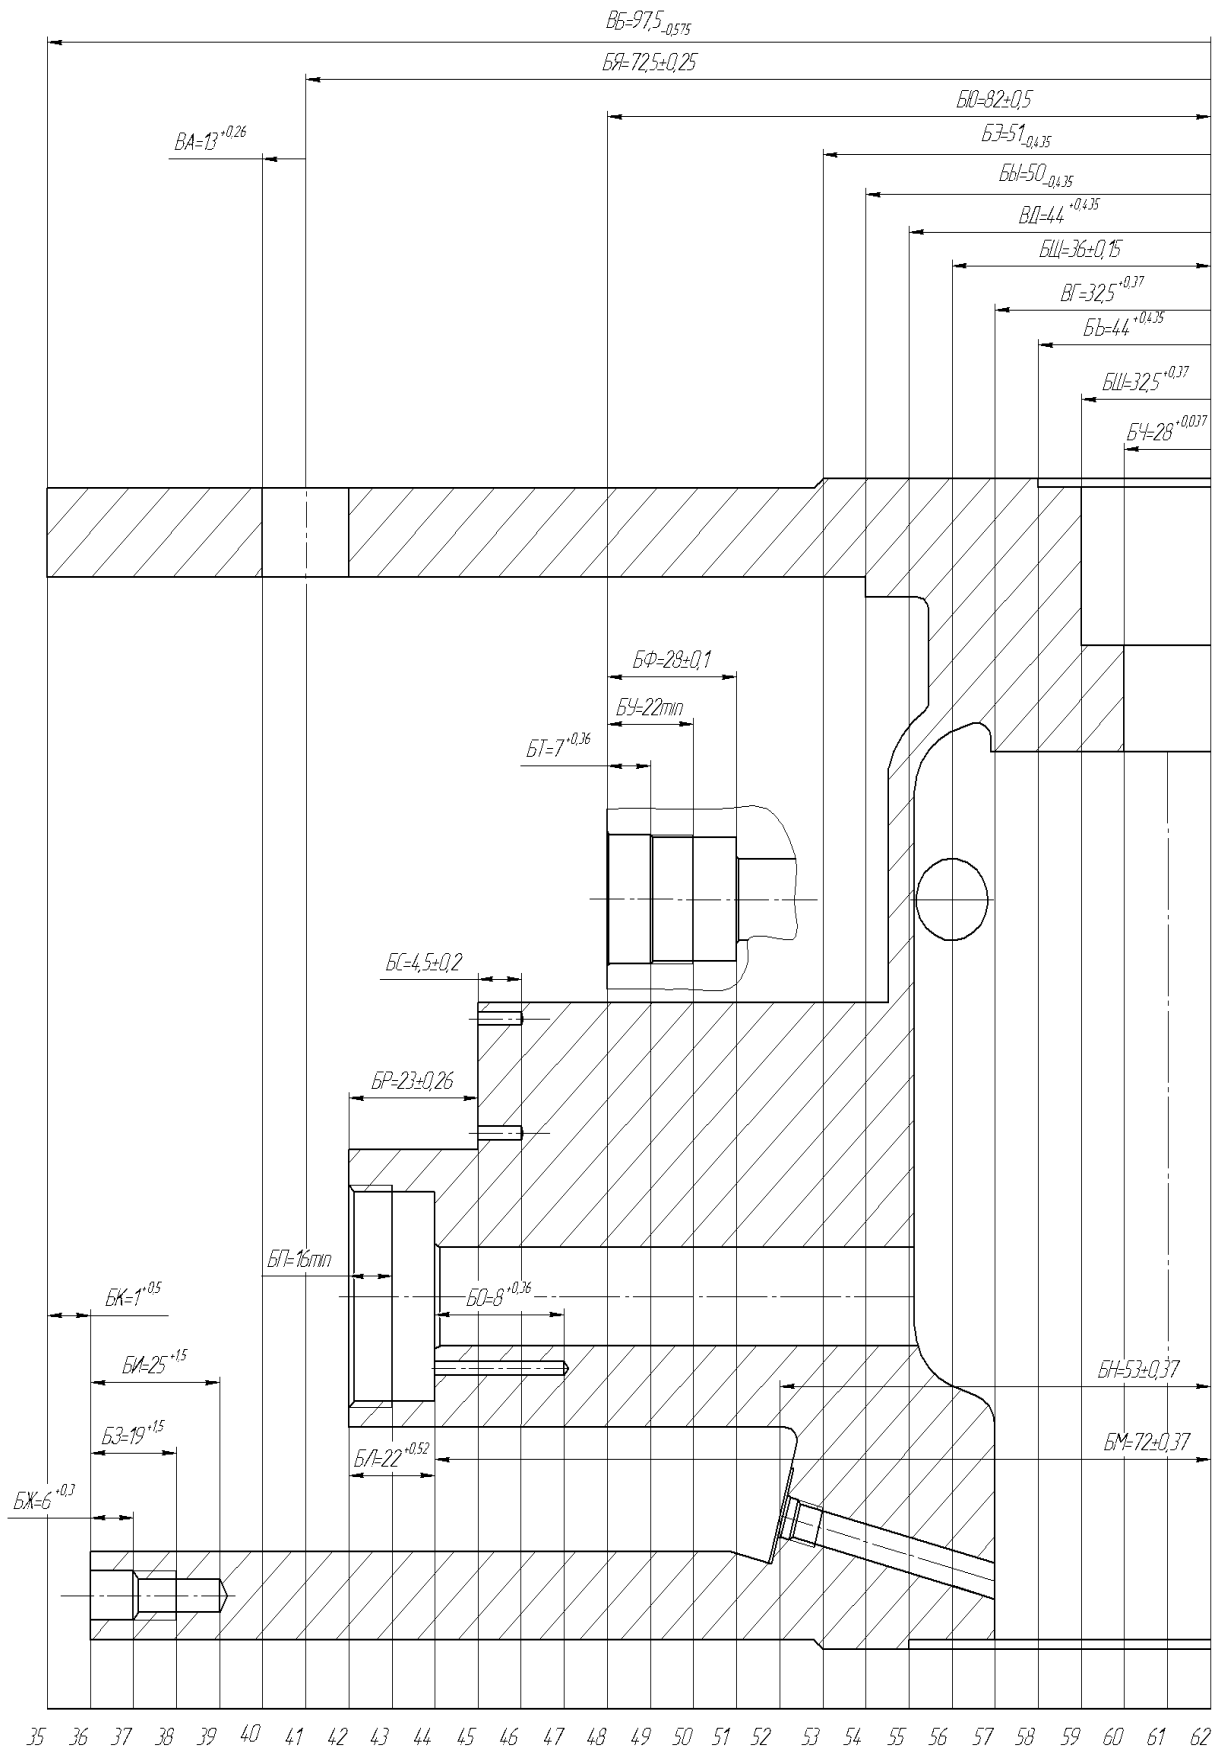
Преобразованный чертеж детали «Корпус» во второй проекции
